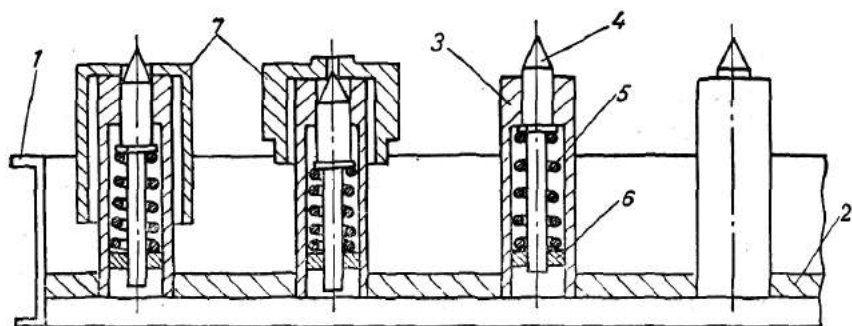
Касета з рухомими базуючими елементами для завантаження деталями типу стаканів:
